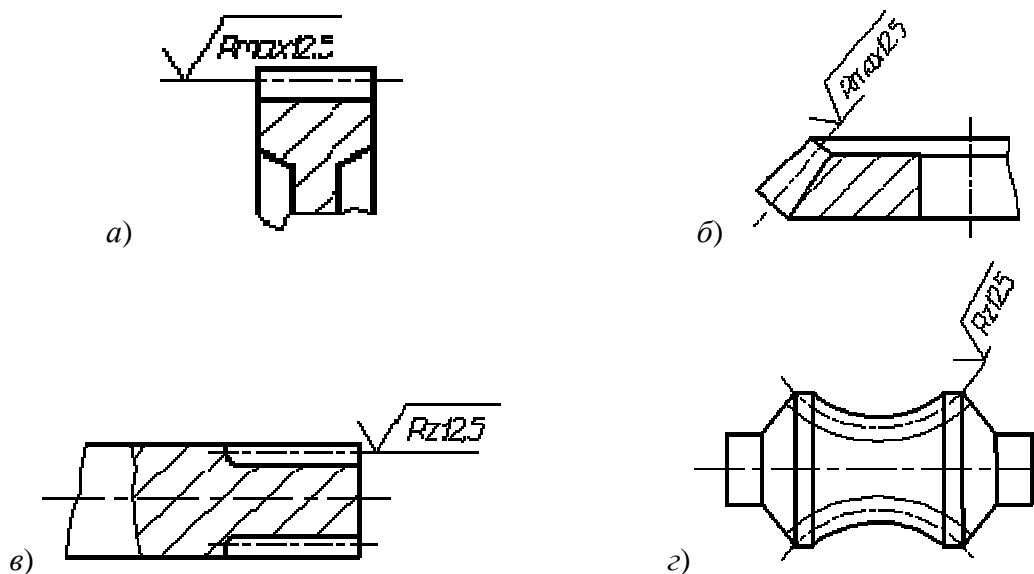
Примеры обозначения шероховатости рабочих поверхностей зубьев: а – цилиндрическое колесо; б – коническое колесо; в – шлицевой вал; з – червяк
